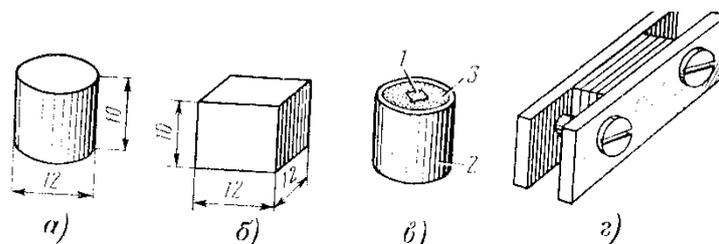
Нормальные размеры металлографических образцов (а и б) и приспособления для приготовления микрошлифов (в и г): 1 – образец; 2 – трубка; 3 – легкоплавкий сплав.
